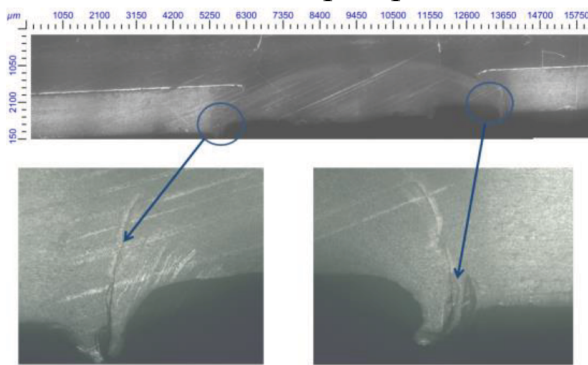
Микроструктура сварного соединения образца № 2 с дефектом «слипание» по кромке сварного соединения.
